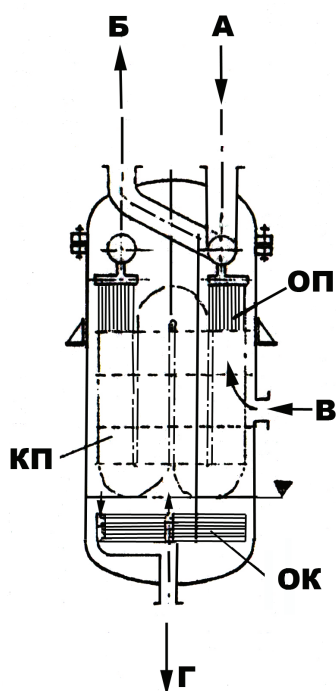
Конструктивная схема подогревателя типа БИП [23]:
